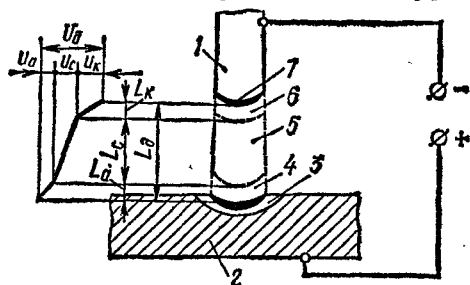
Схема сварочной дуги и падения напряжения в ней:
